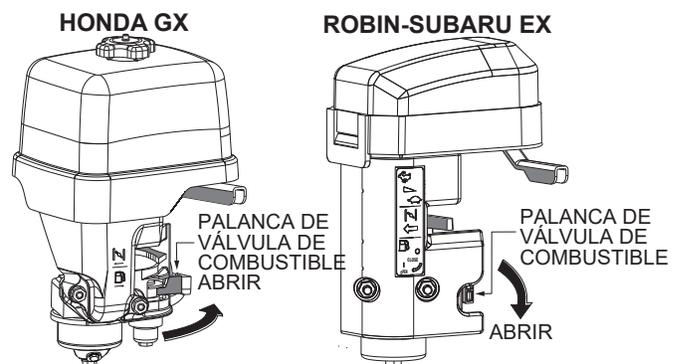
Palanca de la válvula de combustible del motor (ABRIR)
